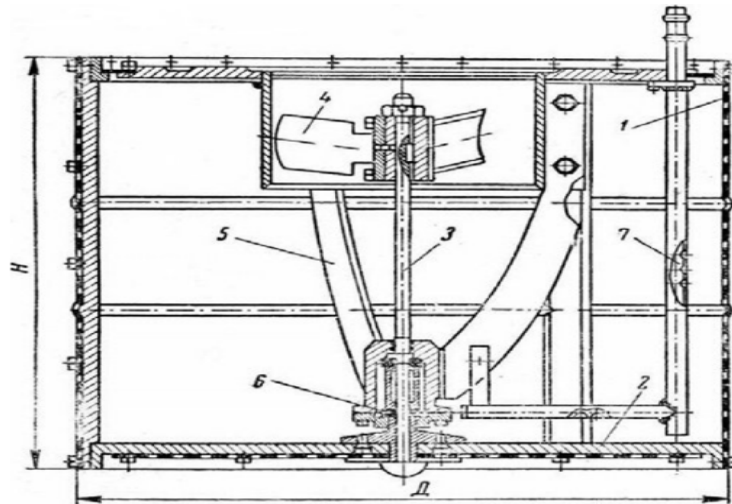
Механічний самоочисний рибозагороджувач з обертовим барабаном від лопатевого гвинта:
